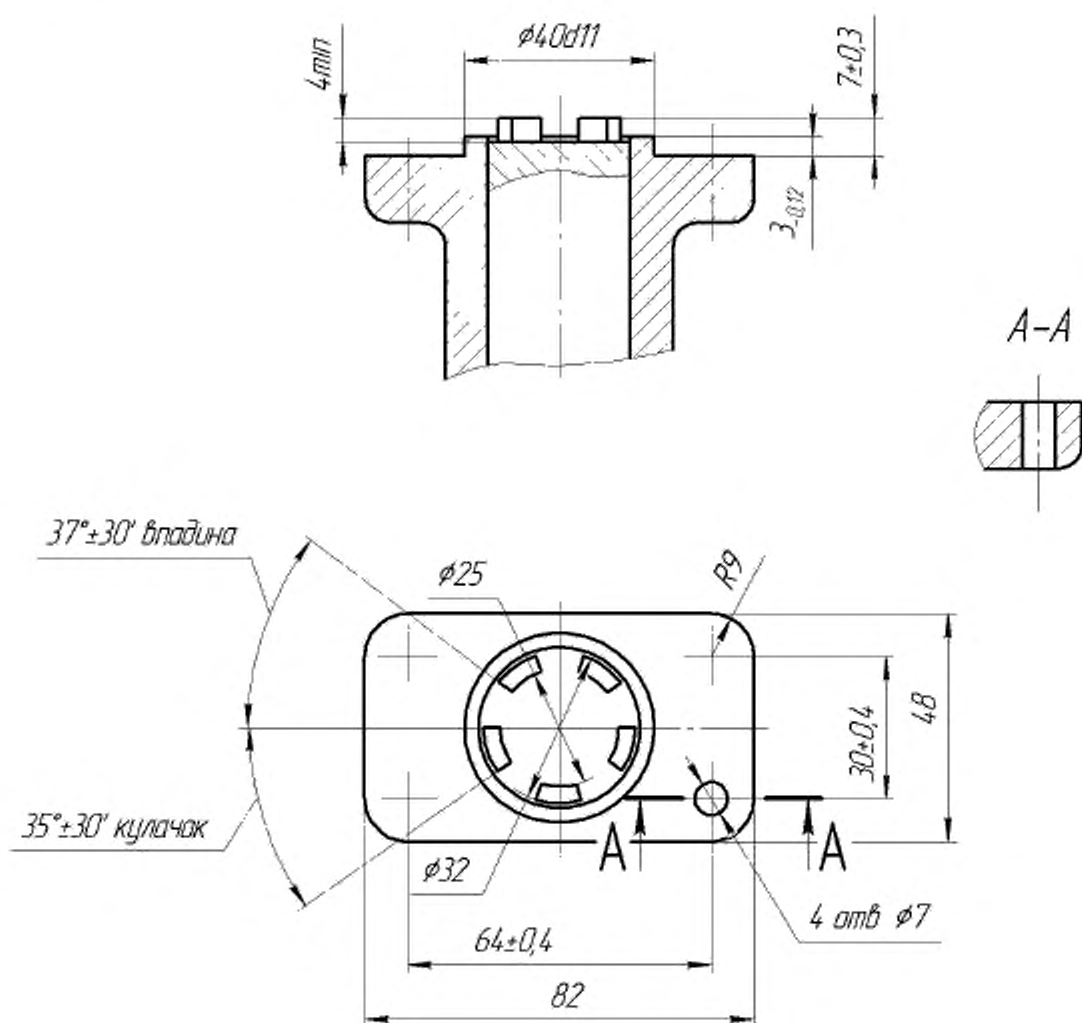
Ответное присоединение трубопроводной арматуры типа МК
